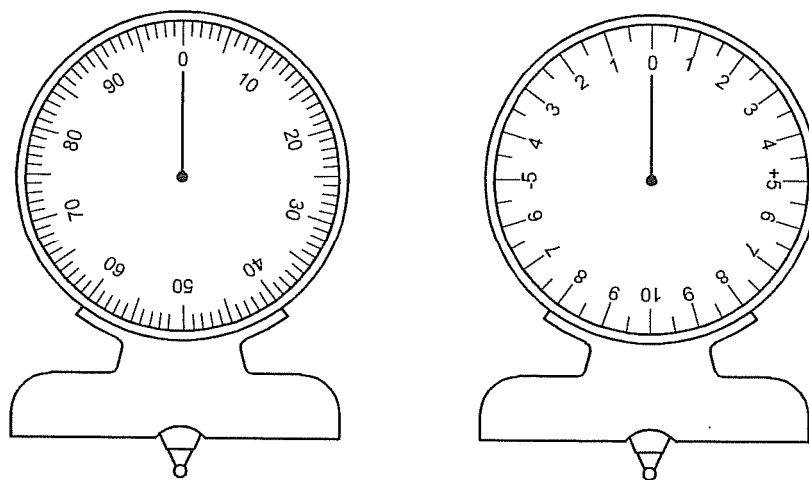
Прибор для измерения высоты профиля резьбы
